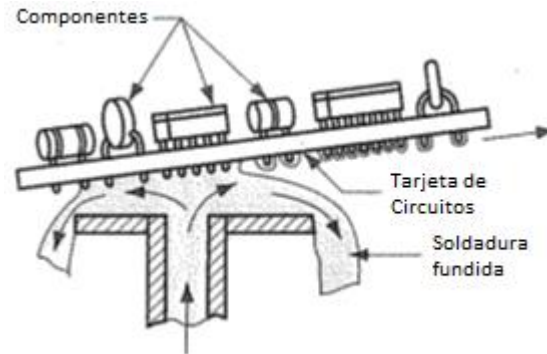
Proceso de soldadura blanda por olas. Tomada de [24].
